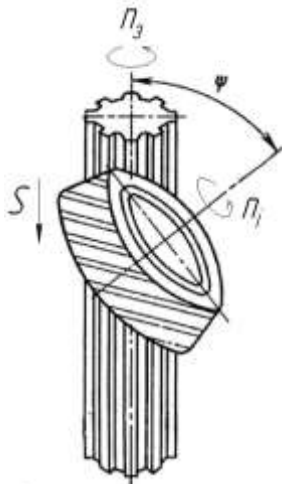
Схема обробки зубів валу зуботочінням:  $n_3$  – напрям обертання заготовки;  $n_i$  – напрям обертання інструменту;  $S$  – напрям подачі
